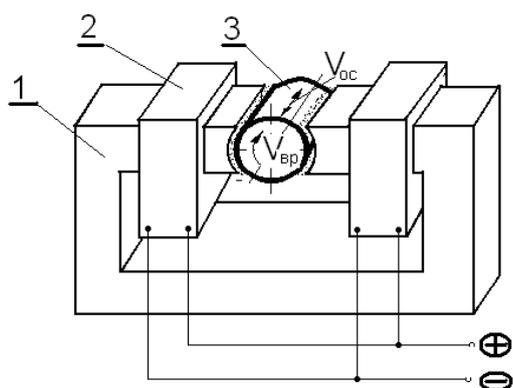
Схема магнитно-абразивного полирования цилиндрической поверхности: 1 – магнитопровод; 2 – катушка электромагнита; 3 – деталь.
